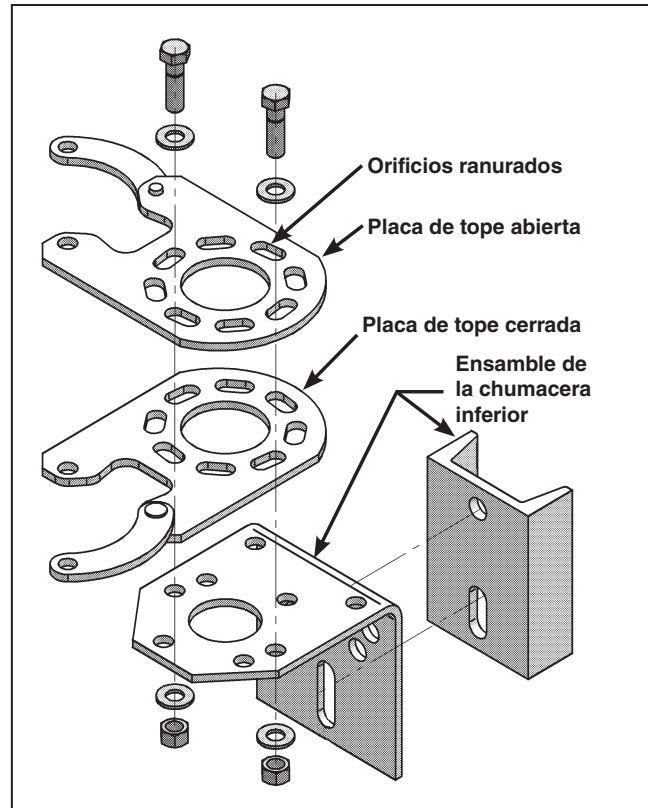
Vista detallada de las placas de tope y el ensamblaje de la chumacera inferior.
